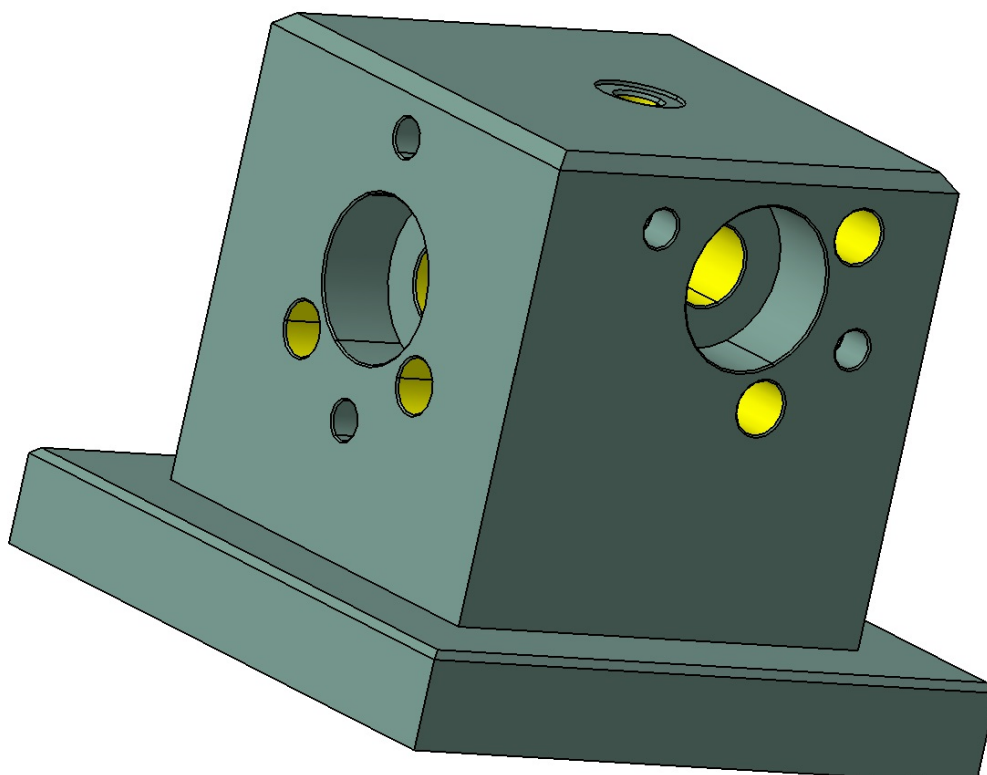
Varianta B – přípravek s ustavenými obrobky
